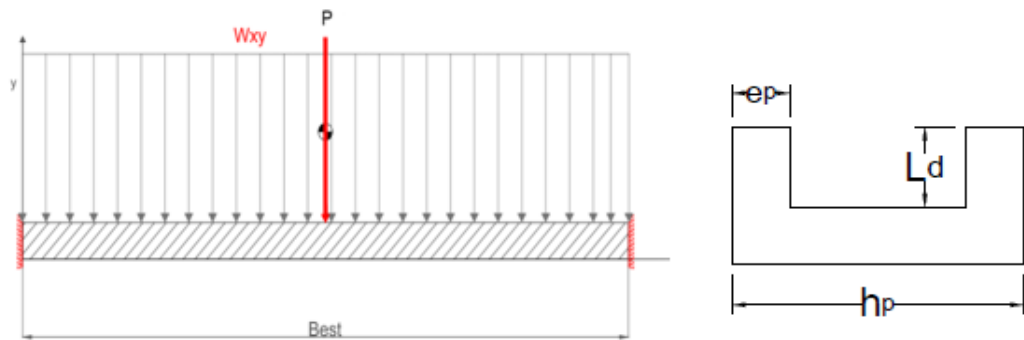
Fuerza aplicada en la paleta y su sección transversal
